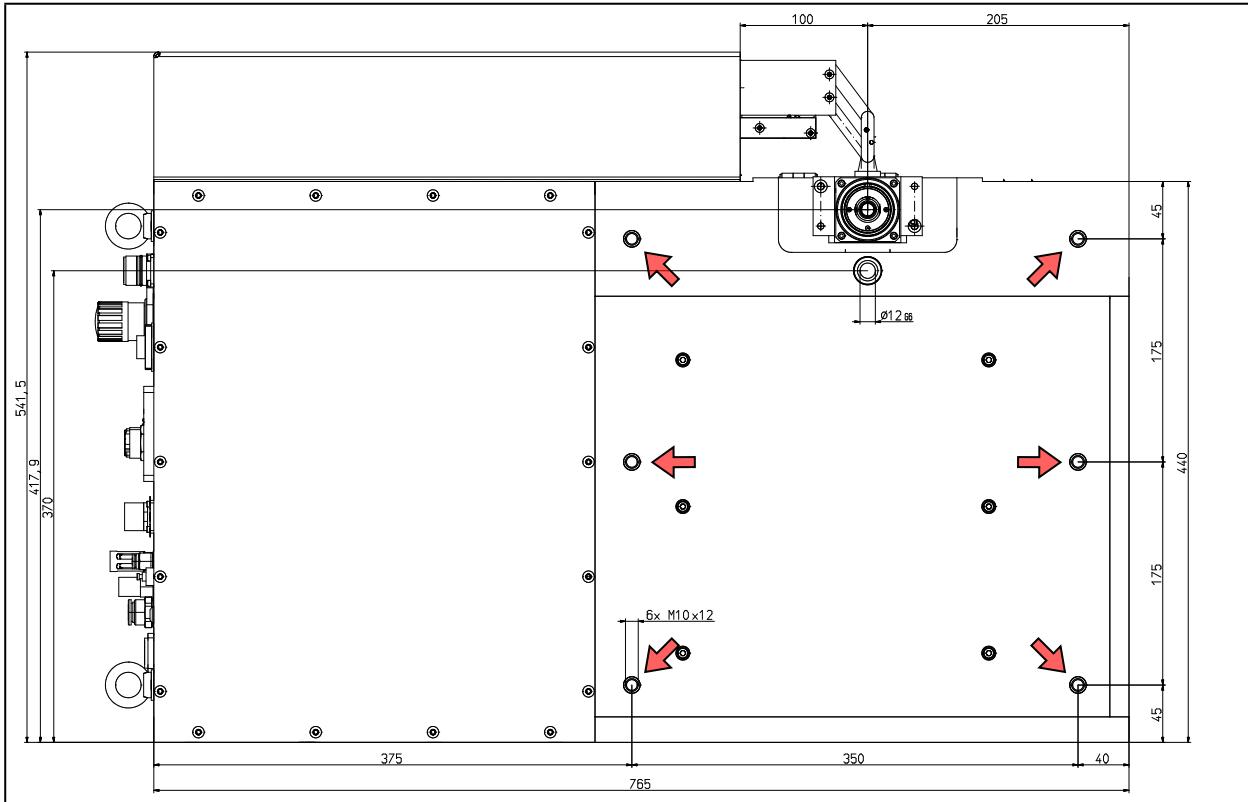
Befestigungsgewinde in der Seitenplatte
